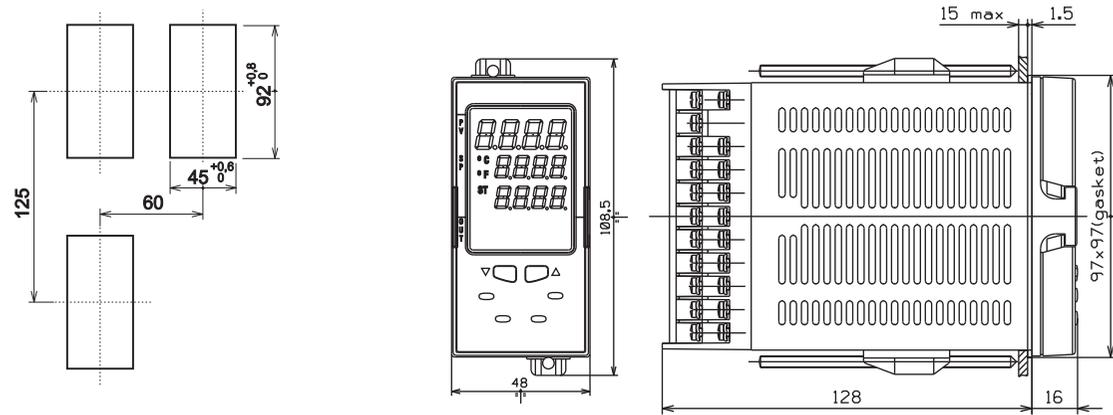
A DIMENSIONI E FORATURA PER PKP
